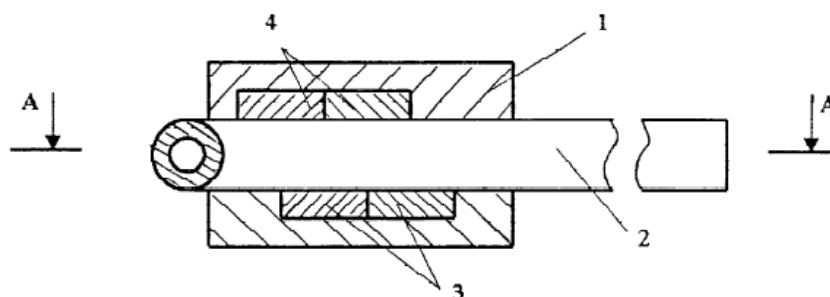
Чертеж магнитоактиватора: 1- корпус; 2 - трубопровод; 3 и 4 - пары магнитов.
